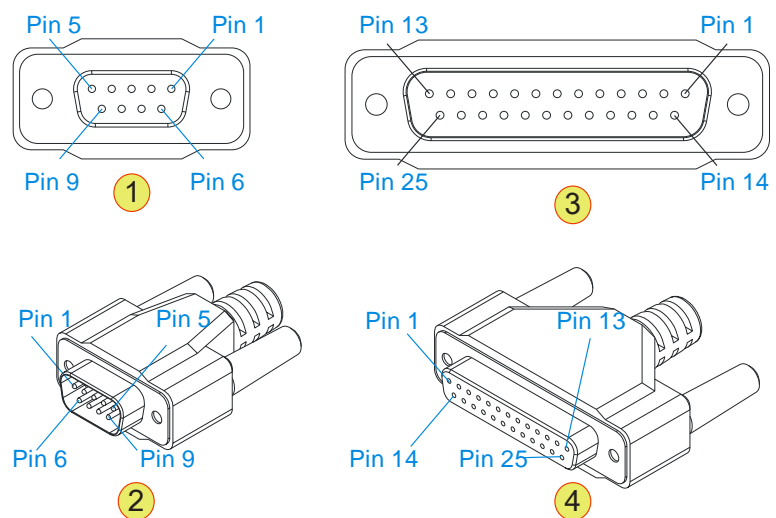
1- D-Sub 9 Pin Buchse; -2- D-Sub 9 Pin Stecker
